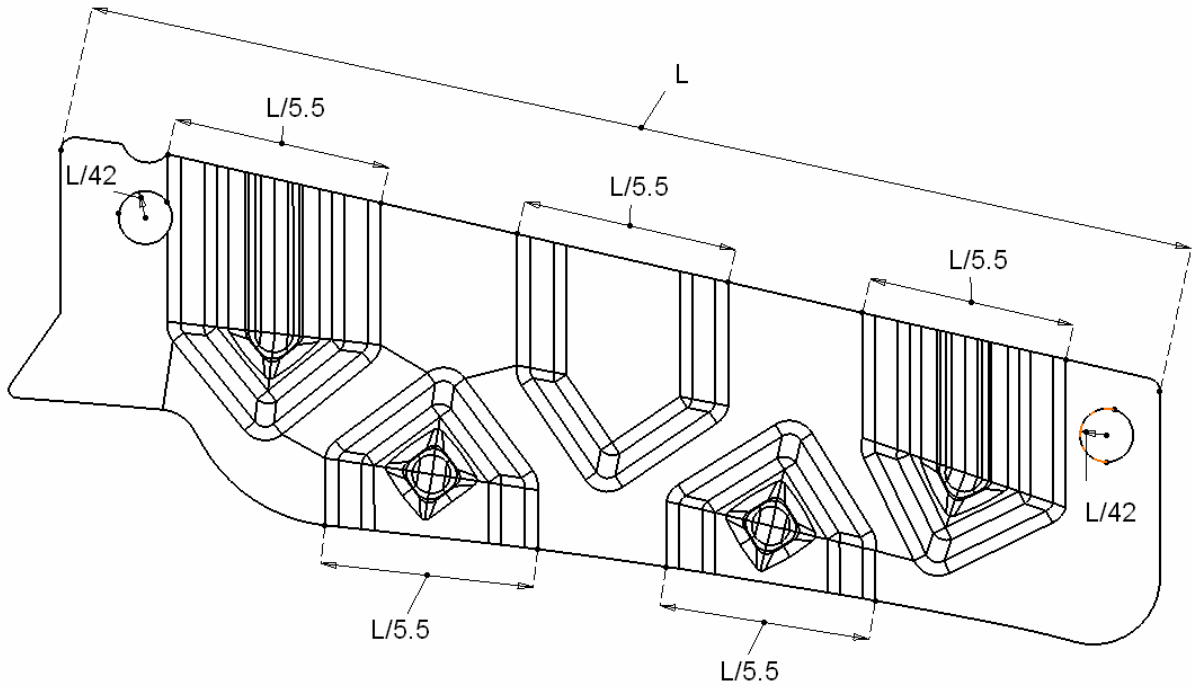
Forme de la pièce et données dimensionnelles en vue de face.
